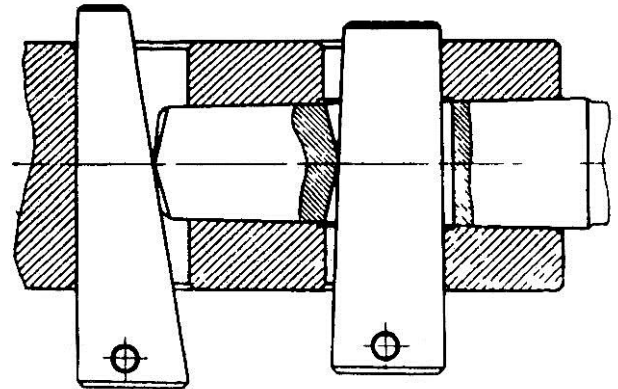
Закріплення інструмента в шпинделі розточувального верстата
